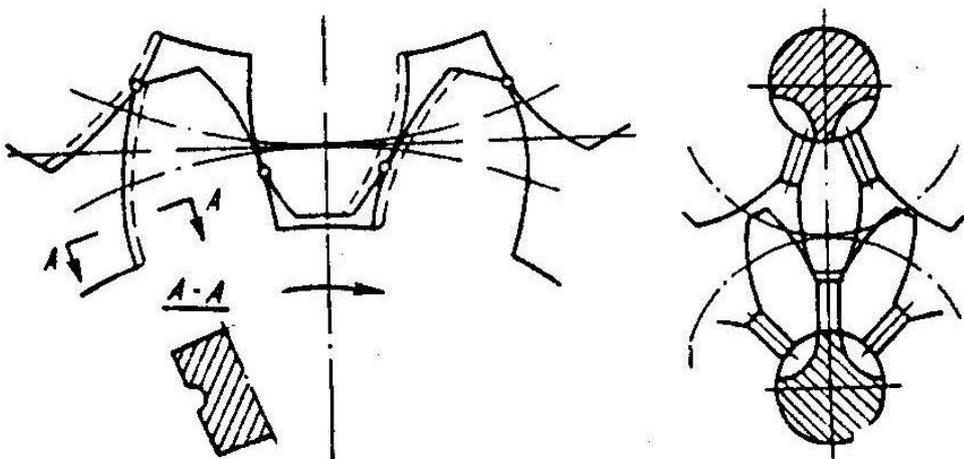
Разгрузочное устройство шестеренных насосов
